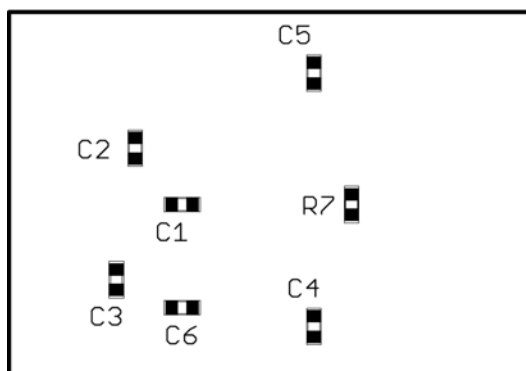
Horní strana desky přípravku pro měření IP_3 (1:1).
